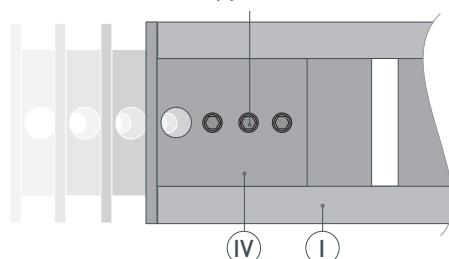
Обрезка лишних частей профиля I и установка заглушки. Вид сверху
